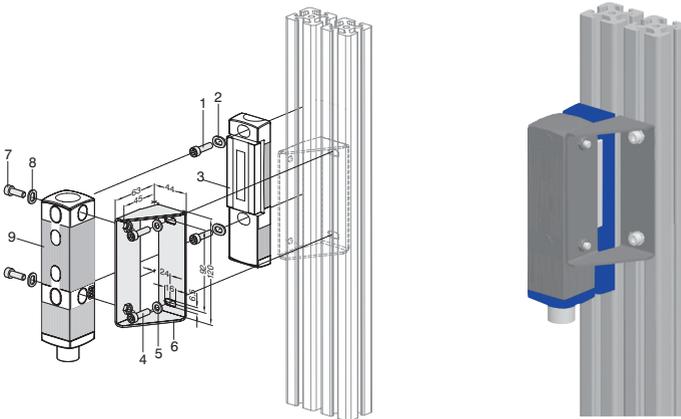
Montaje SD4ICSxxSE89 con ángulo de montaje ZMBSD0001
